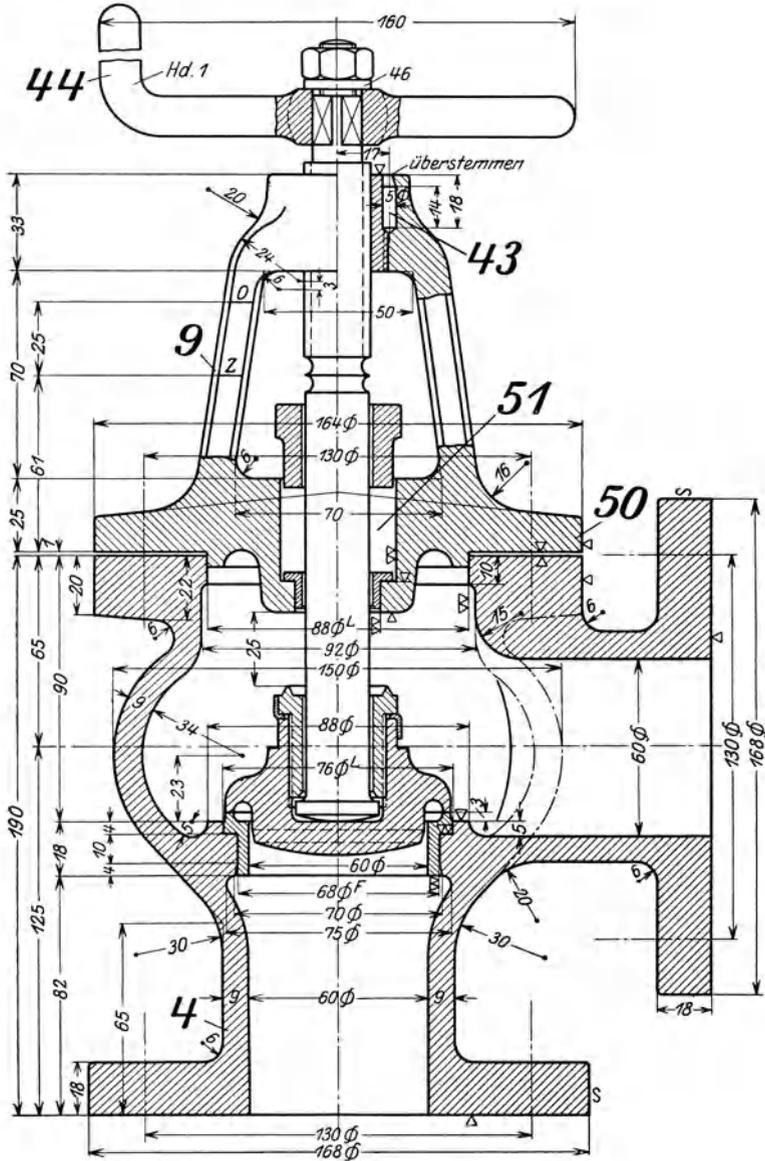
Ausschnitt aus einer Gesamtzeichnung, gleichzeitig Werkzeugzeichnung für Gehäuse und Deckel¹⁾.
